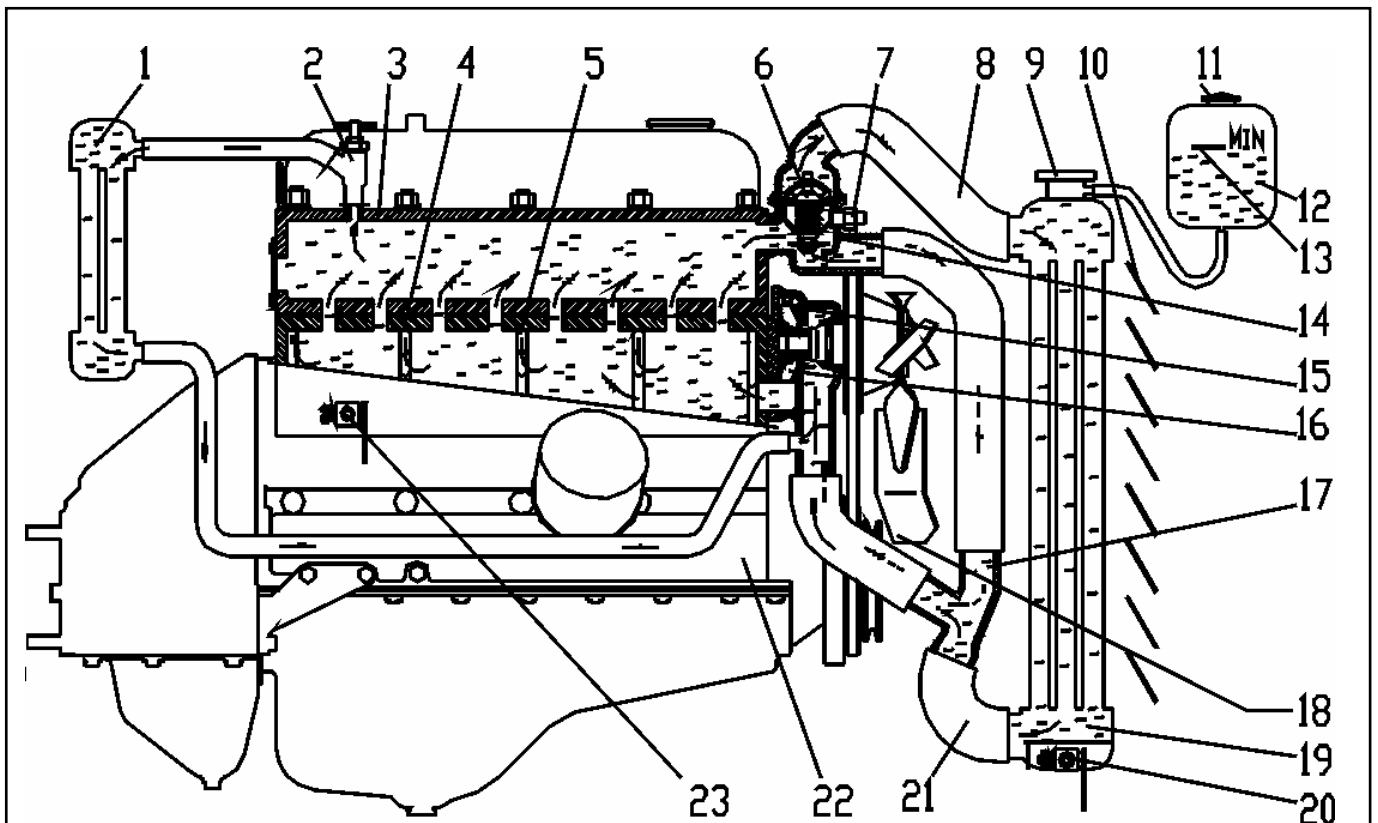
Система охлаждения двигателей для автомобилей “ГАЗель”.
